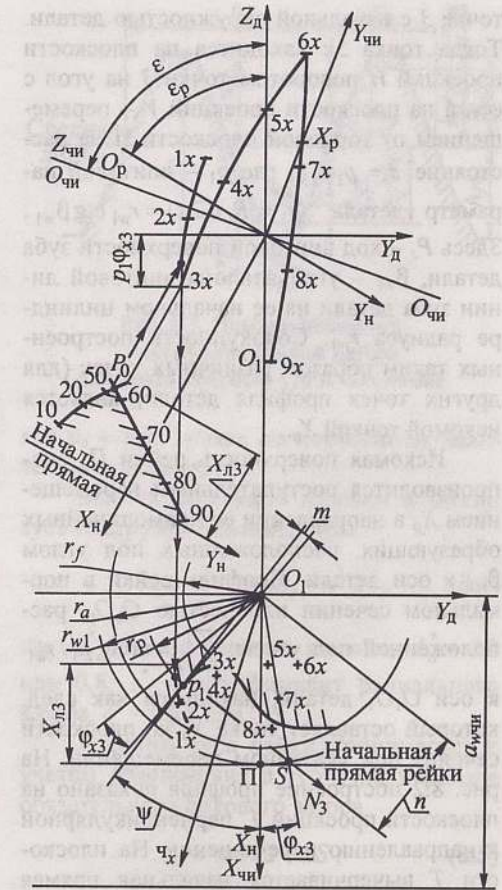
Косозубая инструментальная рейка для деталей произвольного профиля
